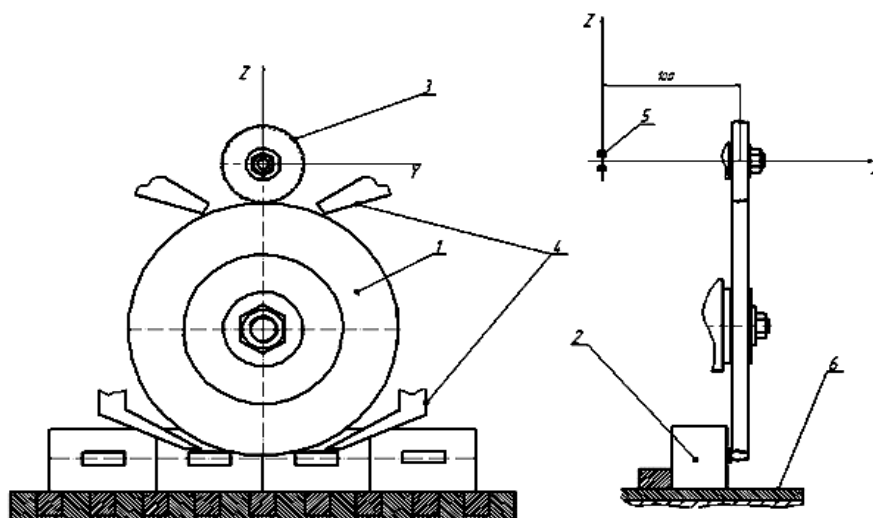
Схема глубинного шлифования на станке ЛШ-220: 1 - шлифовальный круг; 2 - кассета с деталью; 3 - правящий ролик; 4 - сопла для СОЖ; 5 - подшипник, 6 – стол
